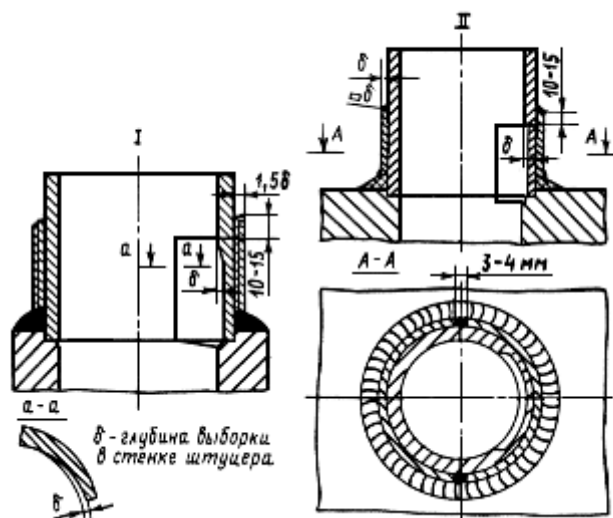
Ремонт штуцеров барабанов: I - наплавка на наружной поверхности штуцера; II - установка бандажа на штуцер
